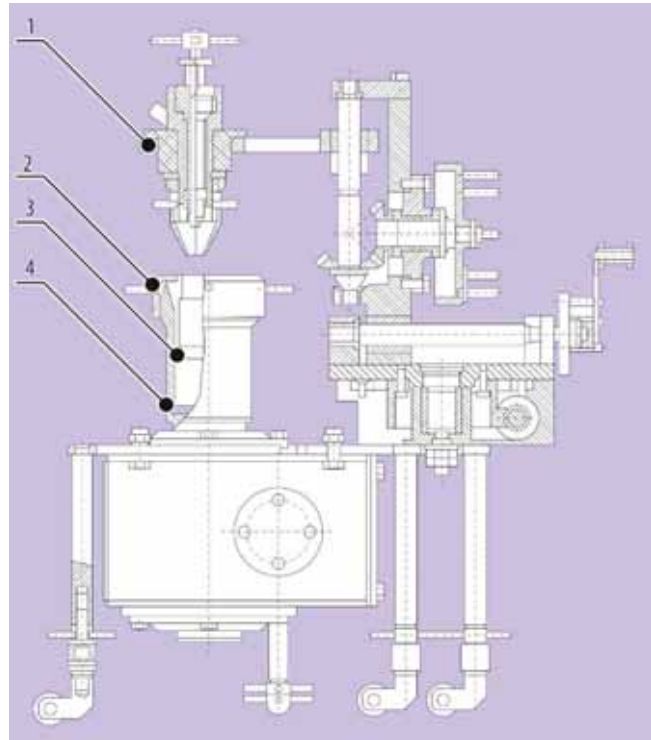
Схема установки сварки кольцевых швов:
